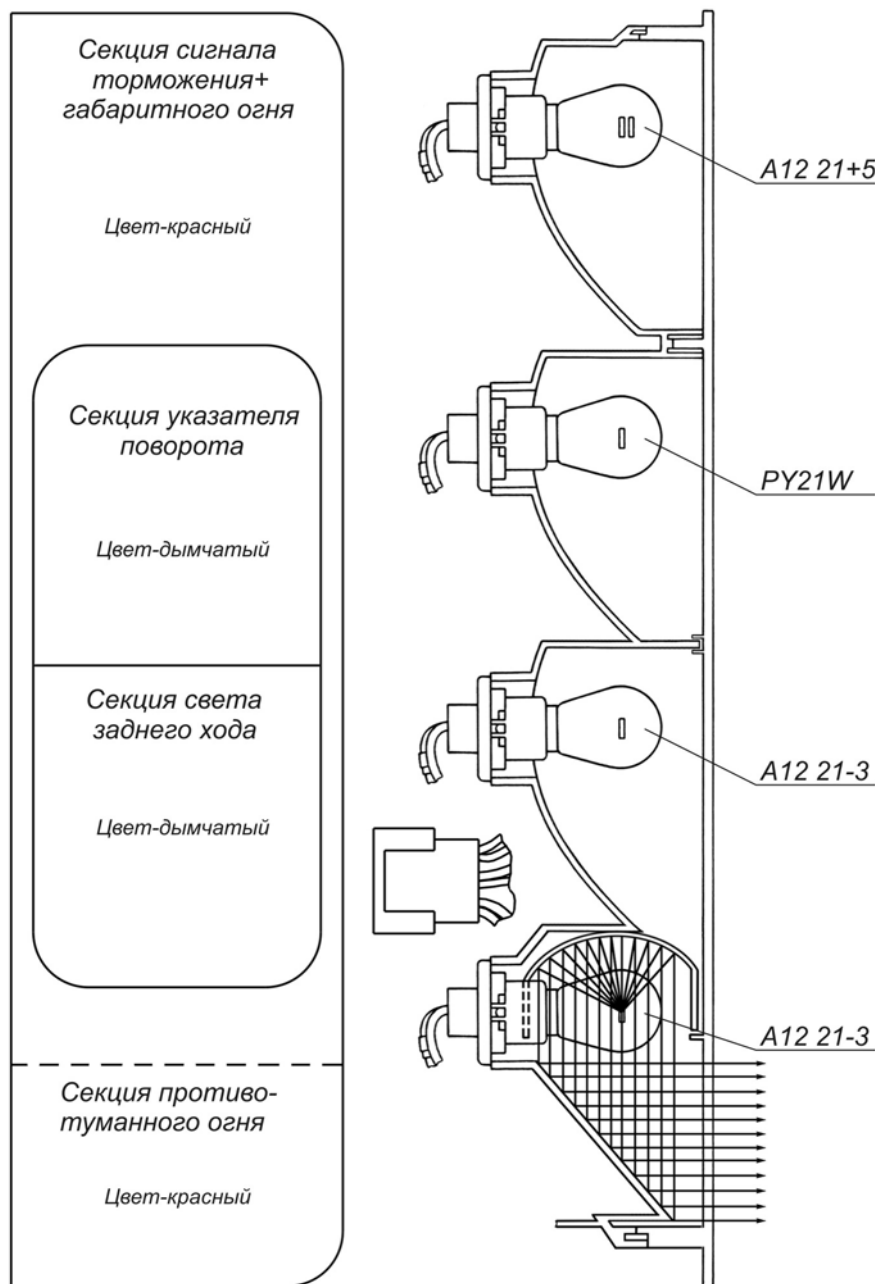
Задний фонарь типа 2705-3716010, 2705-3716011
